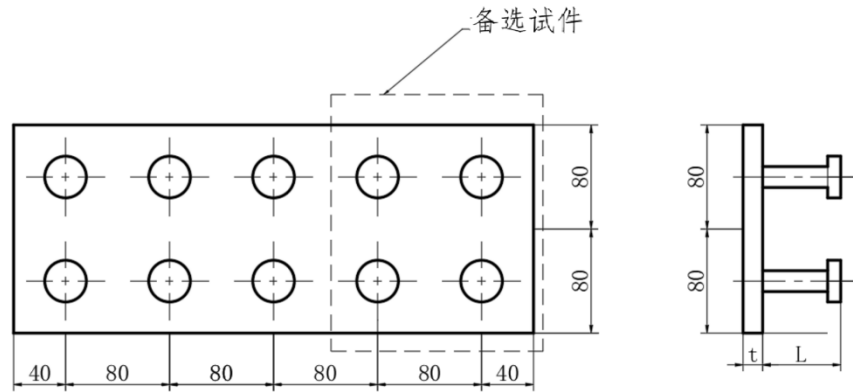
焊钉焊评定试件尺寸
